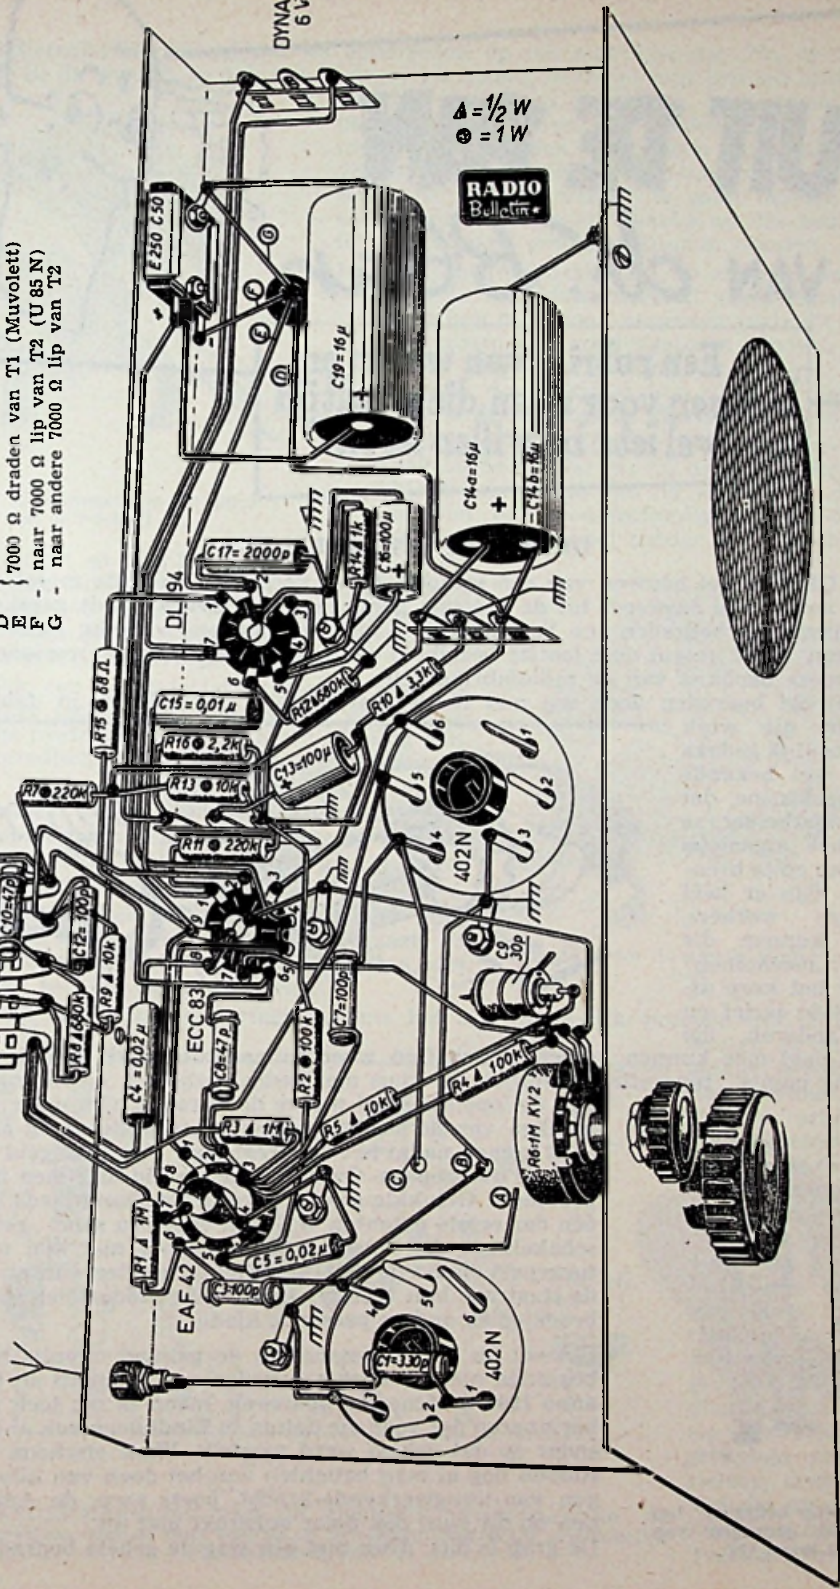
MONTAGEPLAN VAN DE UN-45
